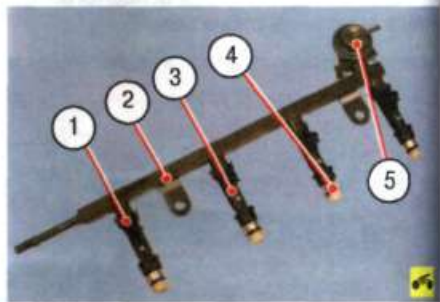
Топливная рампа: 1 – фиксатор форсунки; 2 – рампа; 3 – форсунка; 4 – уплотнительное кольцо форсунки; 5 – регулятор давления топлива
